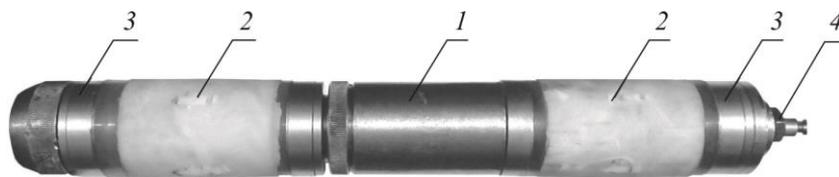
Общий вид надувного пакера: 1 — корпус; 2 — полиуретановая полуvtулка; 3 — опорное кольцо; 4 — штуцер
